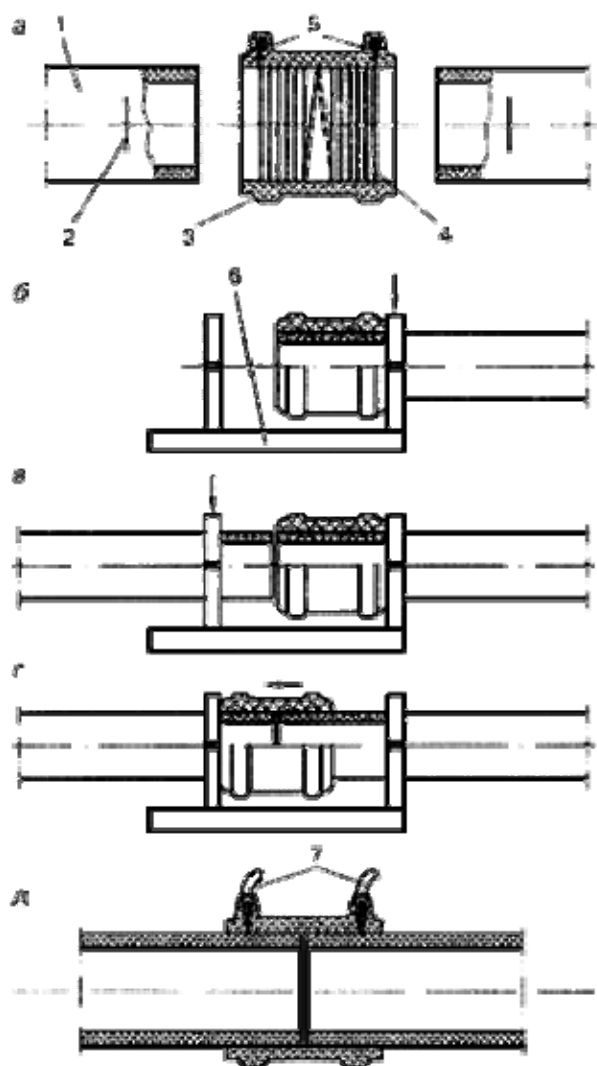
Схема сварки труб с использованием муфт с закладным нагревателем
